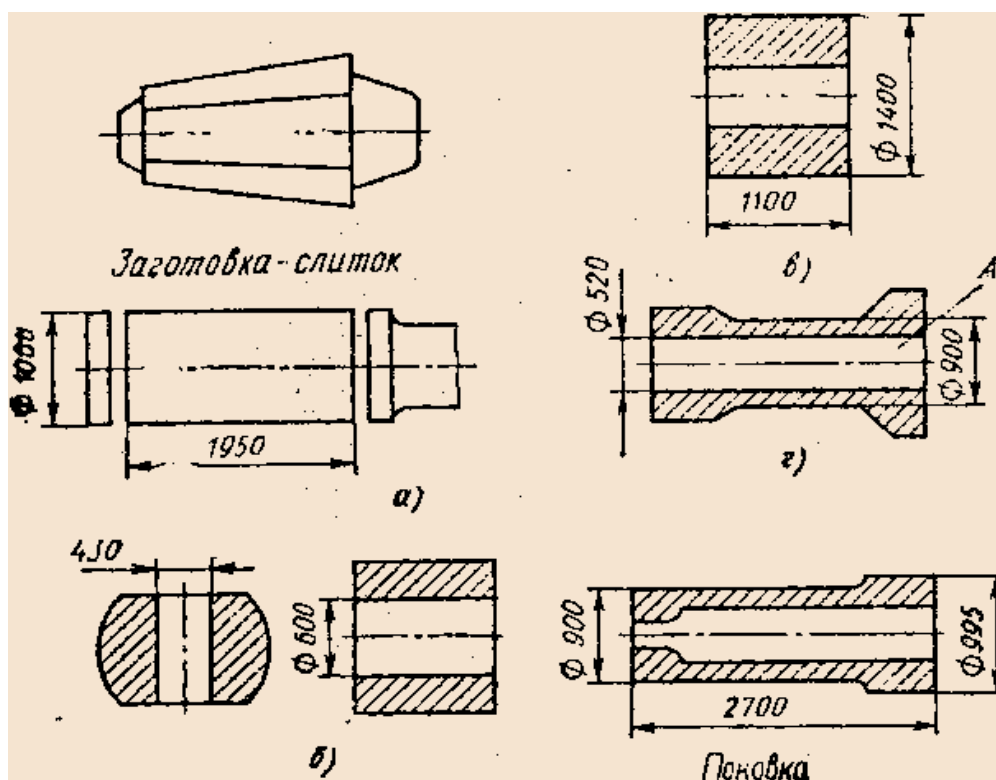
Последовательность операций ковки полого цилиндра из слитка
